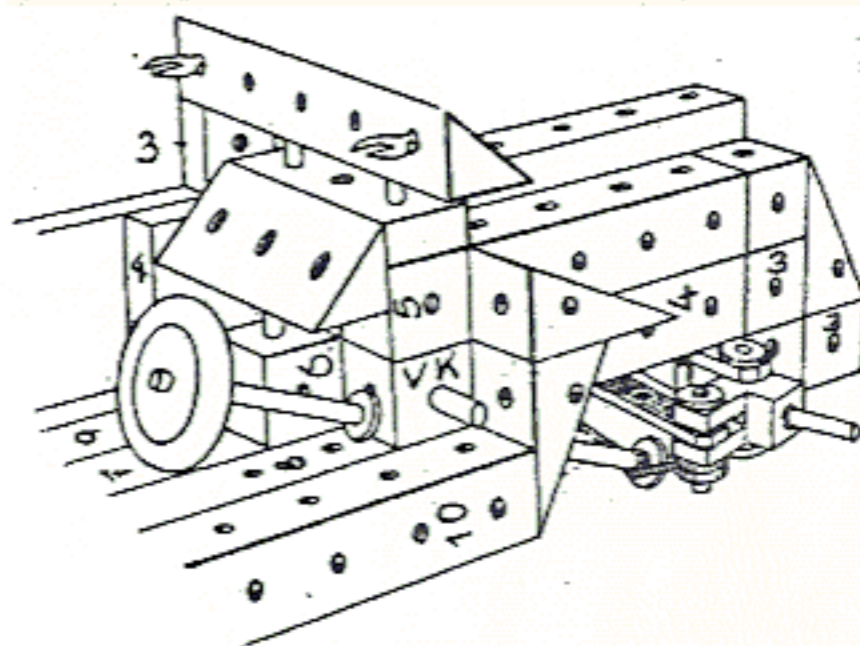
Innenansicht. Schaltbrett und Lenkung.
